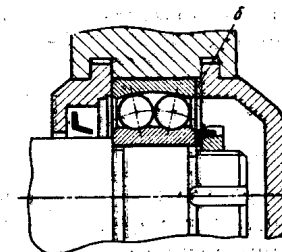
Крепление подшипника между двумя врезными крышками
